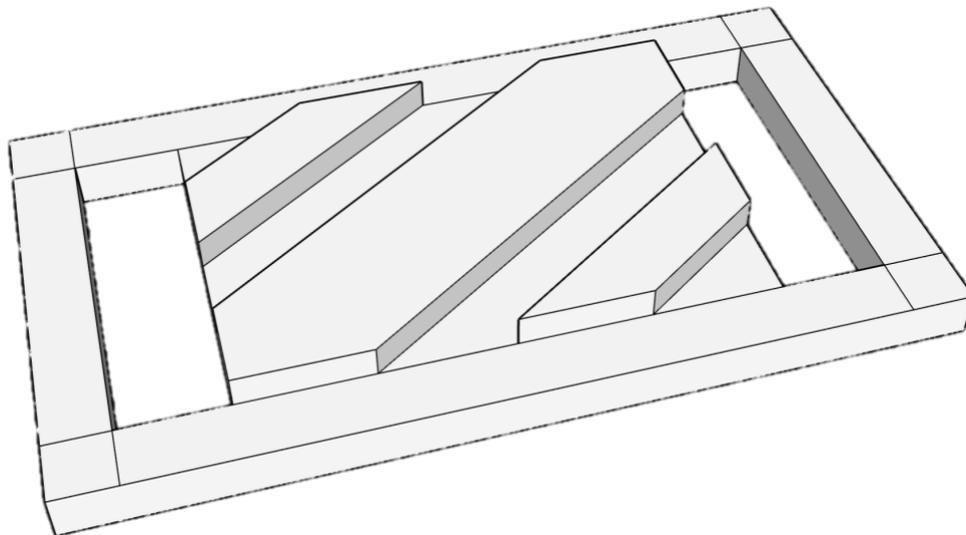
Zapata metálica derecha. Elaboración propia.
